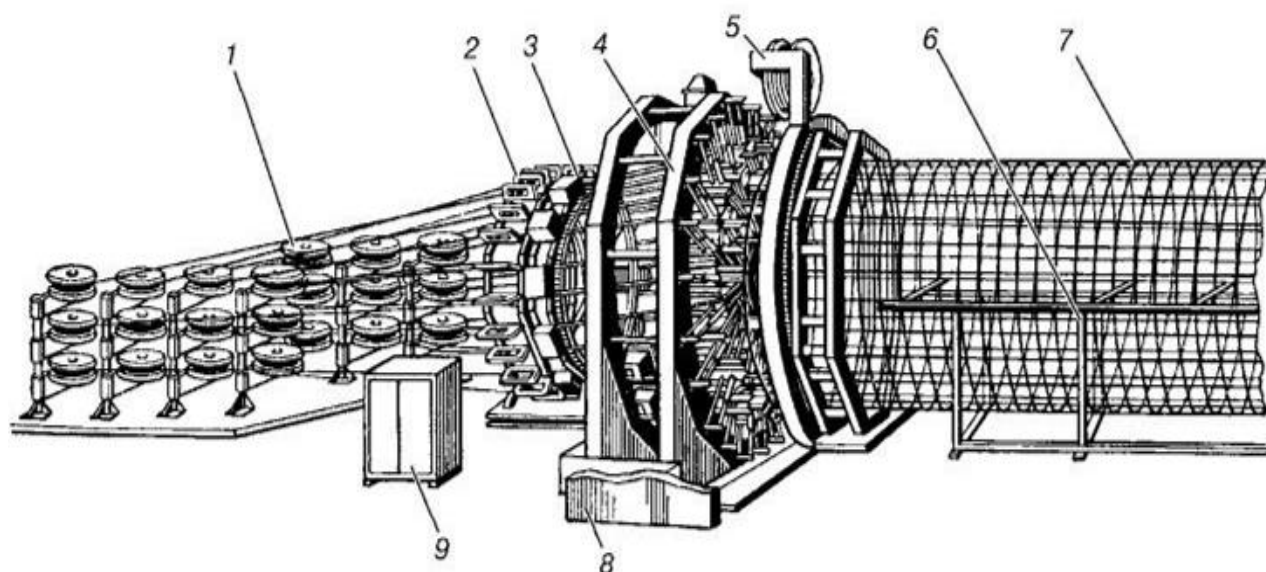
Оборудование для сварки арматурных каркасов
